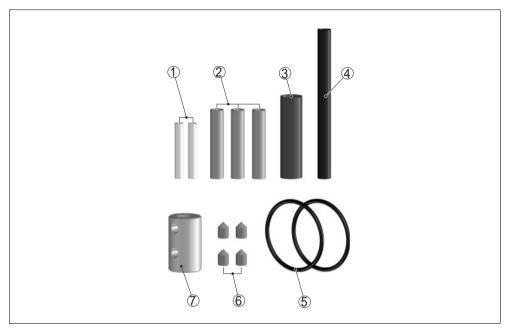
Juego de reducción de cable para VEGAVIB 62
